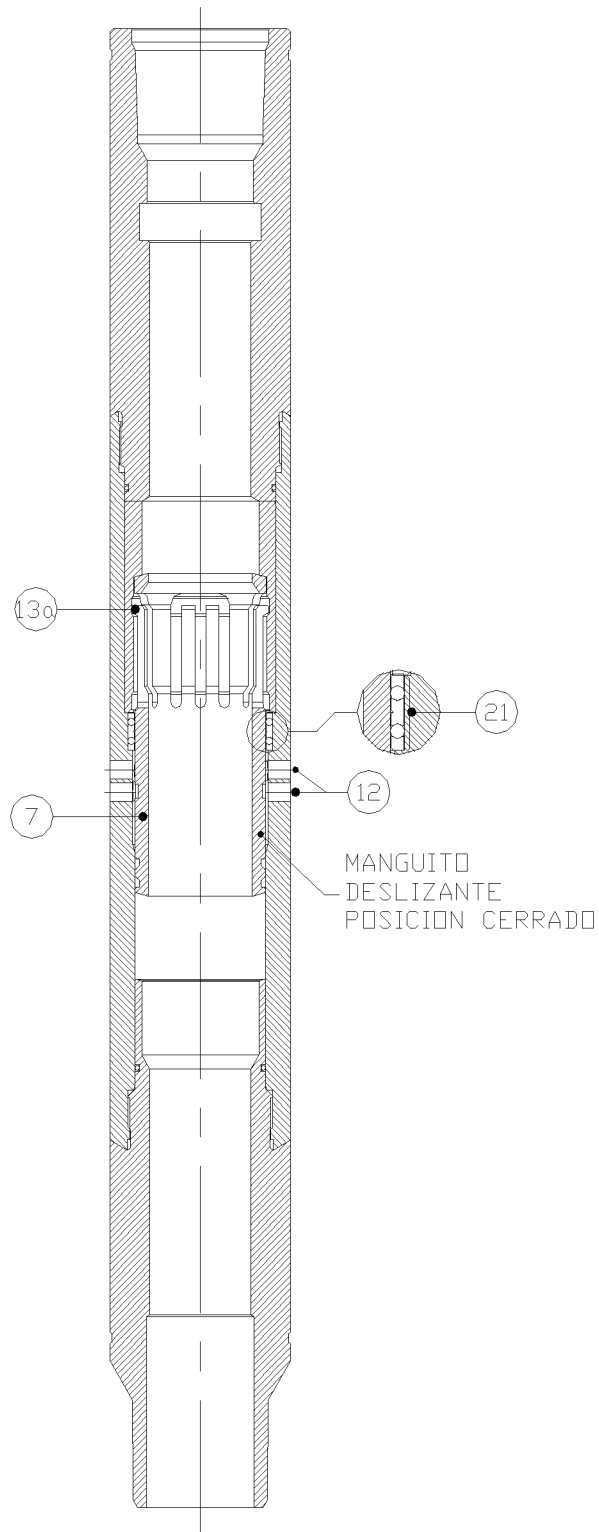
VISTA EN SECCIÓN AXIAL LONGITUDINAL DE LA CAMISA DE CIRCULACIÓN CON EL MANGUITO DESLIZANTE EN POSICIÓN CERRADA
